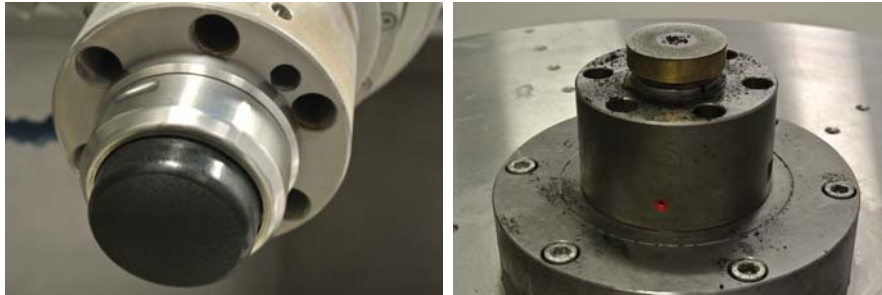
Frézovací nástroj s vázaným diamantovým zrnem.
